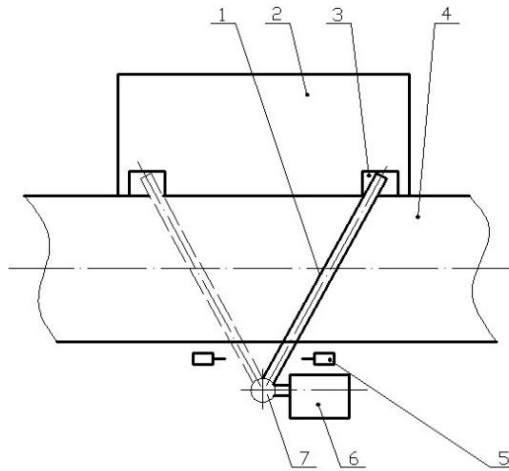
Плуговий скидач: 1 – плуг; 2 – приймальний бункер; 3 – електромагнітний пристрій фіксатору; 4 – конвеєр; 5 – електроперемикач; 6 – двигун-редуктор; 7 – зубчата передача
